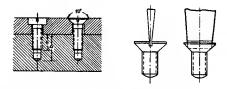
Ausführung versenkter Schraubverbindungen (links); sa muß der Schraubenzieher passen, damit der Schraubenkapf nicht verletzt wird (rechts)
